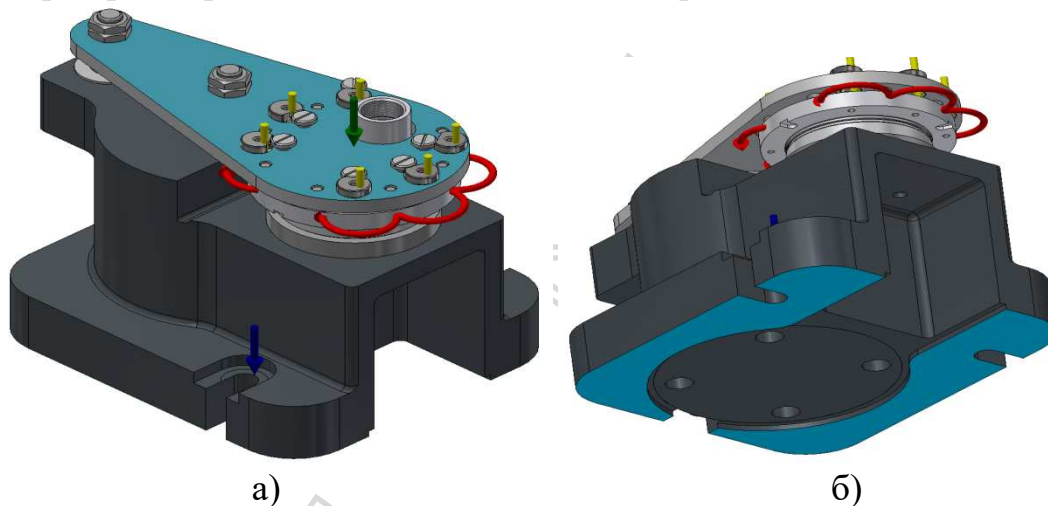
Действия силовых параметров: а) - усилия зажима заготовки детали в кондукторе; б) - выбранные поверхности и грани пневматического кондуктора при закреплении его на столе станка
